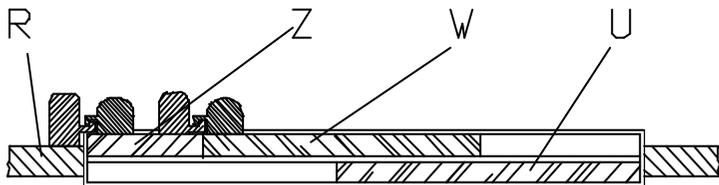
Anordnung mit Einbauteil (Draufsicht)
